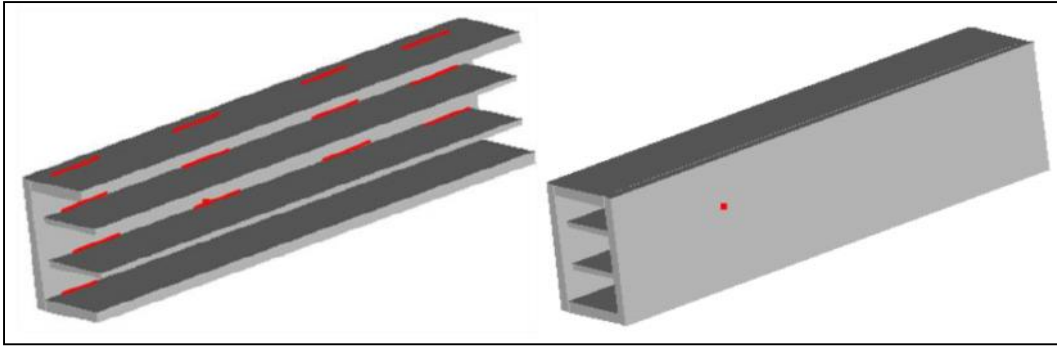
Assemblage des tôles par points de soudure [10]
